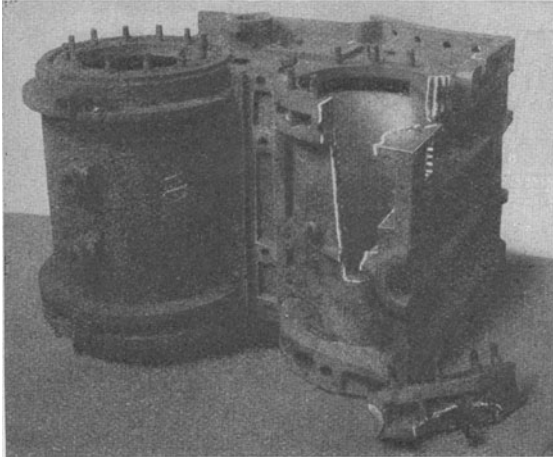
Gerissener Lokomotivzylinder vor der Schweißung.
